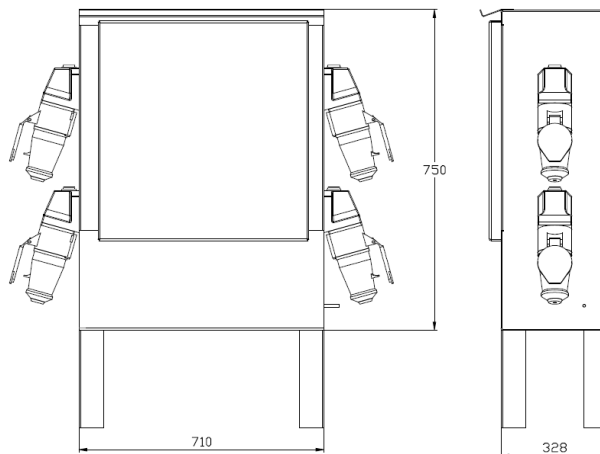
Внешний вид и габаритные размеры шкафа ПРС.
